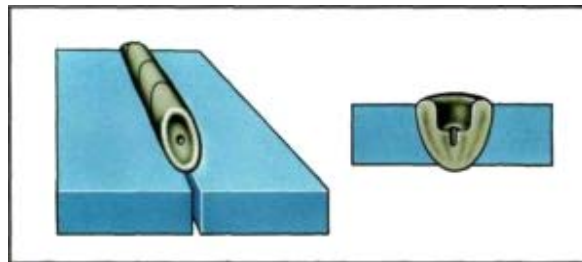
Дефект зварного з'єднання кратери
